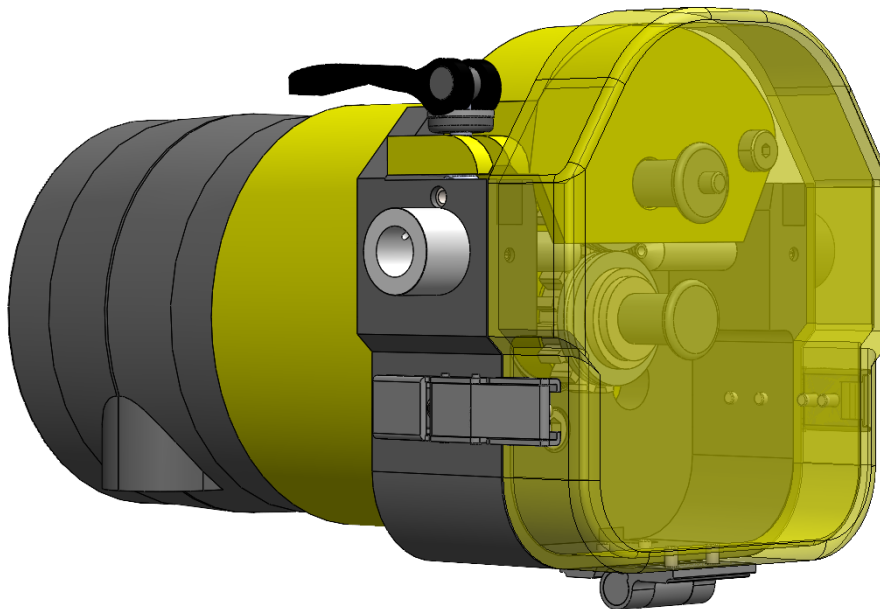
Protótipo final do sistema de alimentação de fio de soldadura
